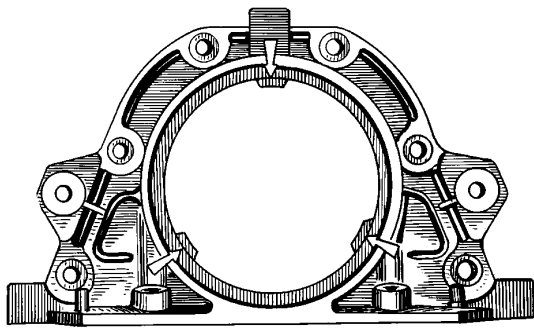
Halter des hinteren Dichtringes der Kurbelwelle
